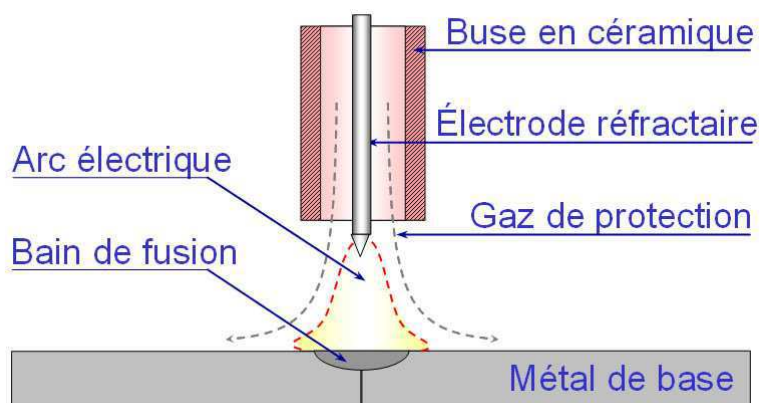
Schéma de principe du soudage TIG
